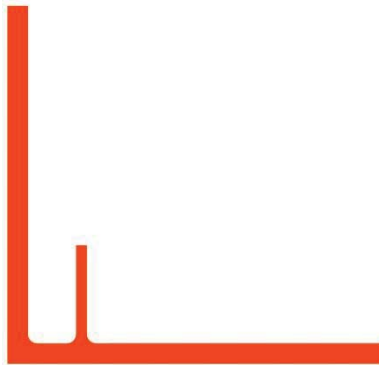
Secção conceptual da peça metálica de apoio dos contrapesos
